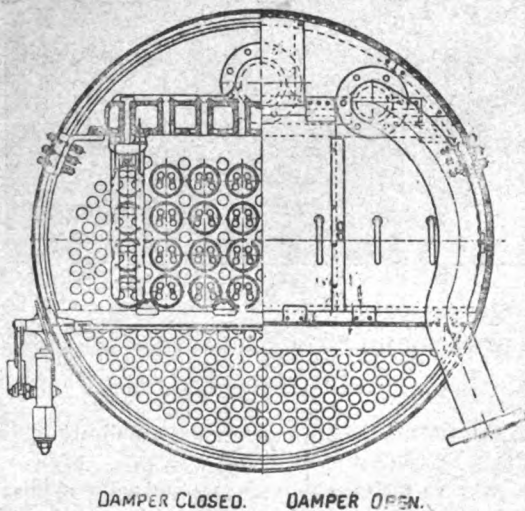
Sezione trasversale — Damper closed = Registro chiuso — Damper open = Registro aperto.
